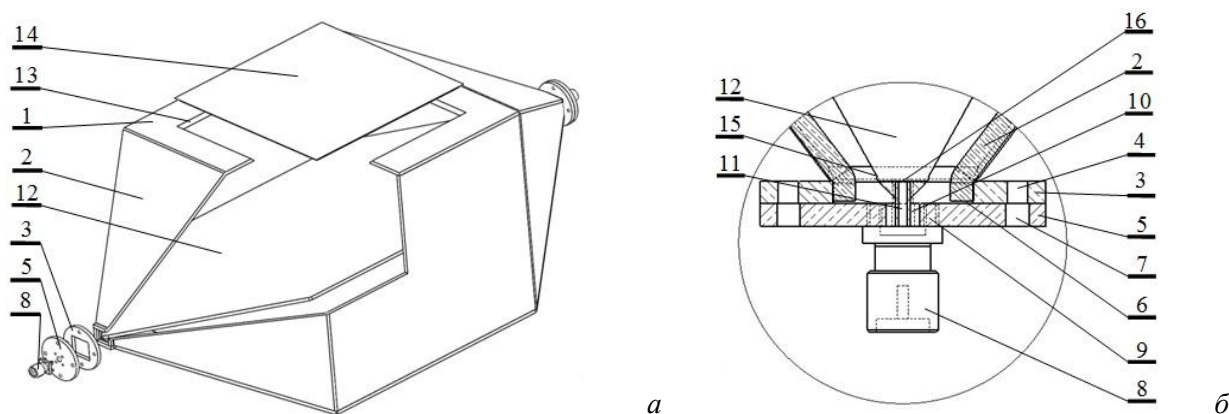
Сборочный чертеж (а) и фрагмент продольного сечения ТЕМ-камеры около СВЧ соединителя (б)
